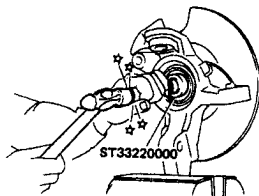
Снятие ступицы и подшипника (См. Раздел 6)
